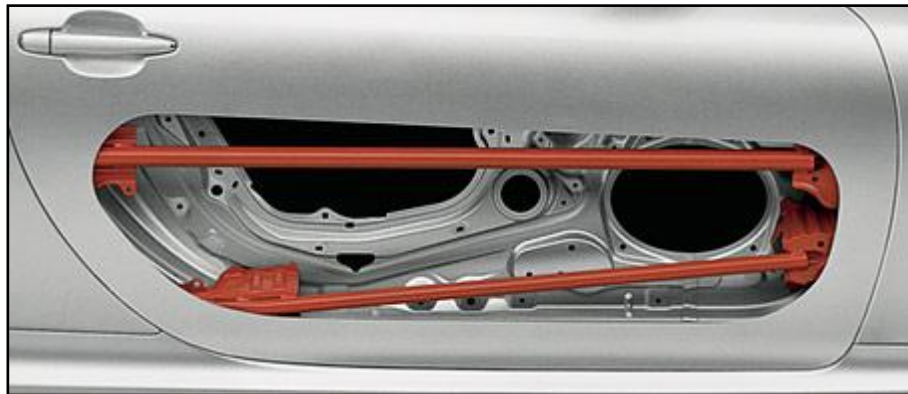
Disposición de las barras de protección lateral en la puerta.
